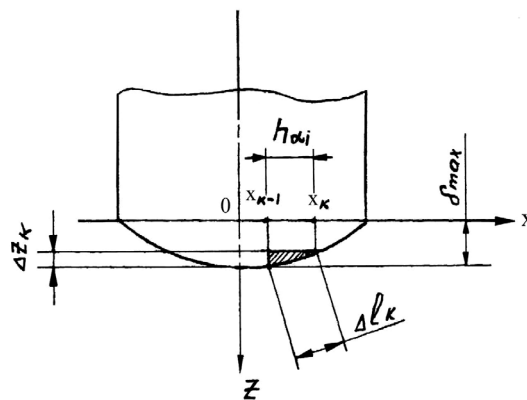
Схема для визначення опуклості торцевої поверхні вальцьованої заготовки
